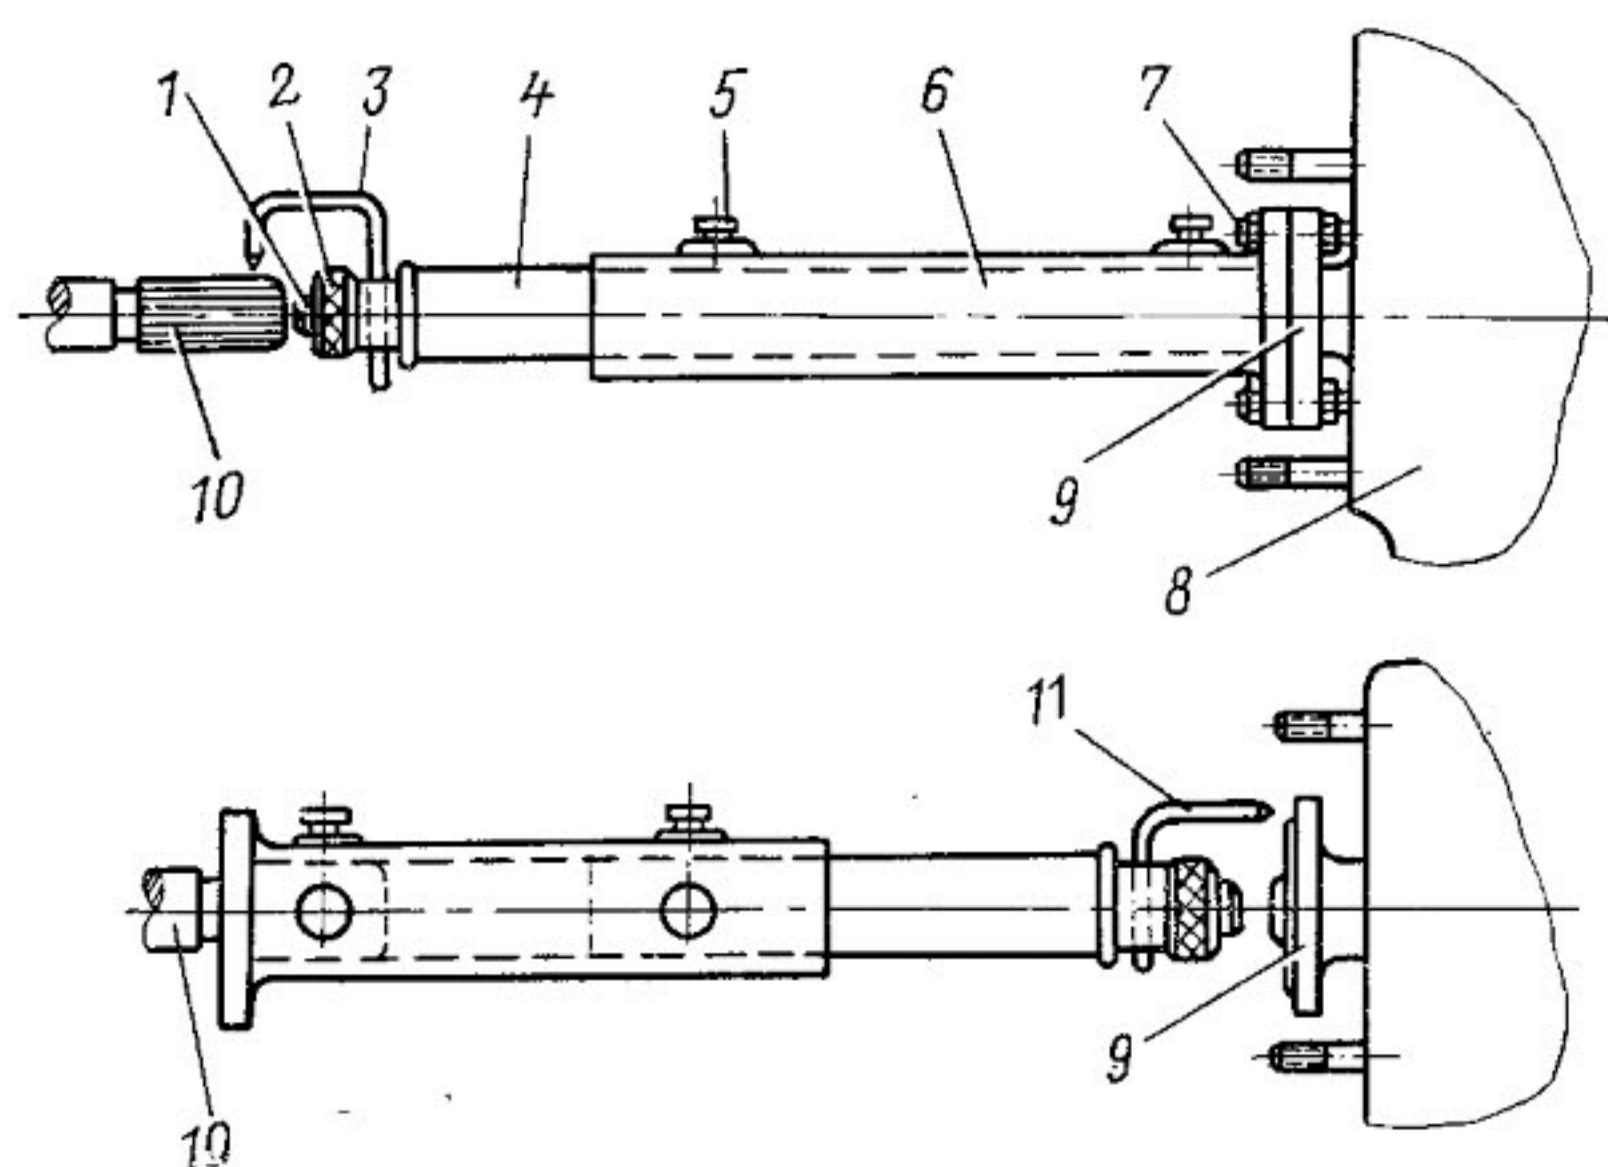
Приспособление для проверки соосности редуктора Р-7 и вентилятора:
